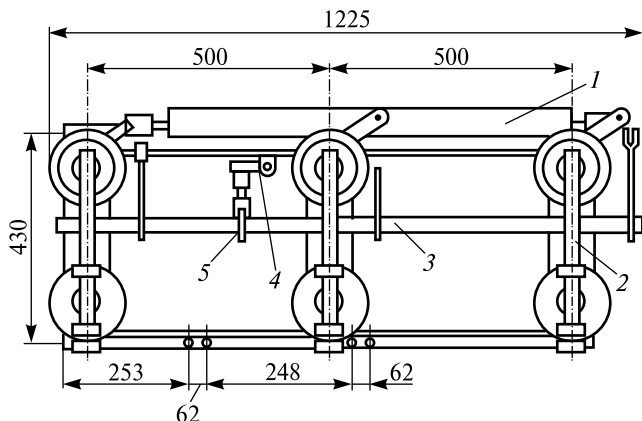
Общий вид разъединителя РЛНД-1-10-400-У1 с одним заземляющим ножом
